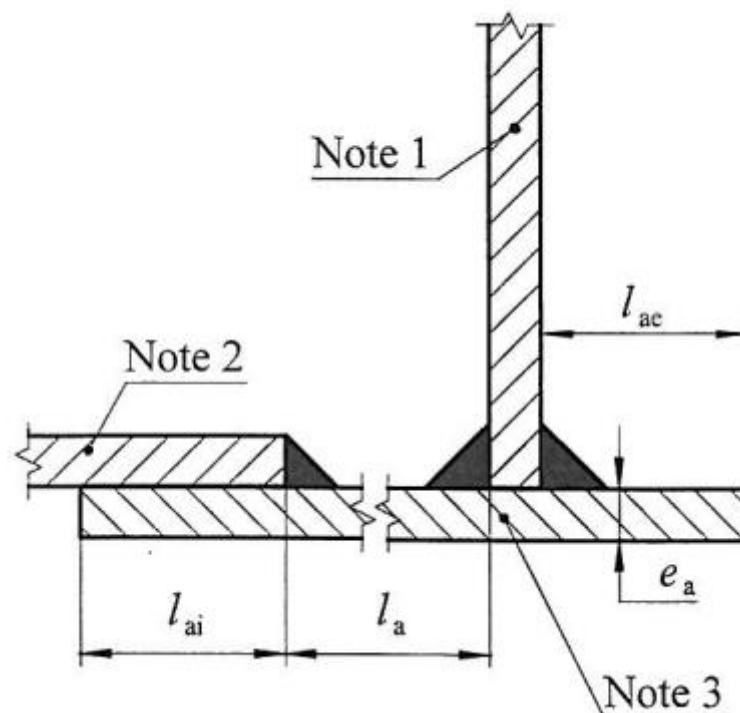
Disposition des tôles de fond assemblées par recouvrement[14]
